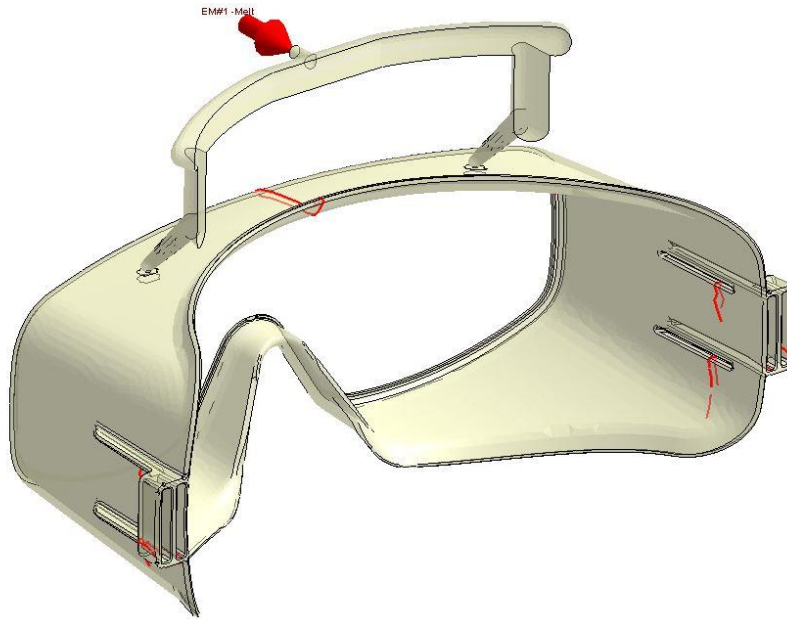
Linhas de soldadura do TPU (a vermelho)
